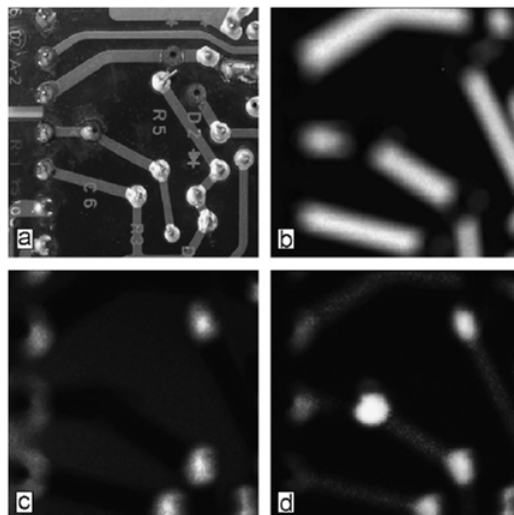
PCB: a) Fotografia do PCB. Distribuição do b)Cu c)Sn d)Pb na placa PCB [5]
